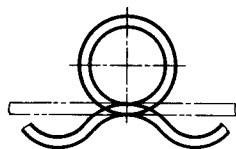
Форма переходов штамповки втулки с применением реверсивной гибки
